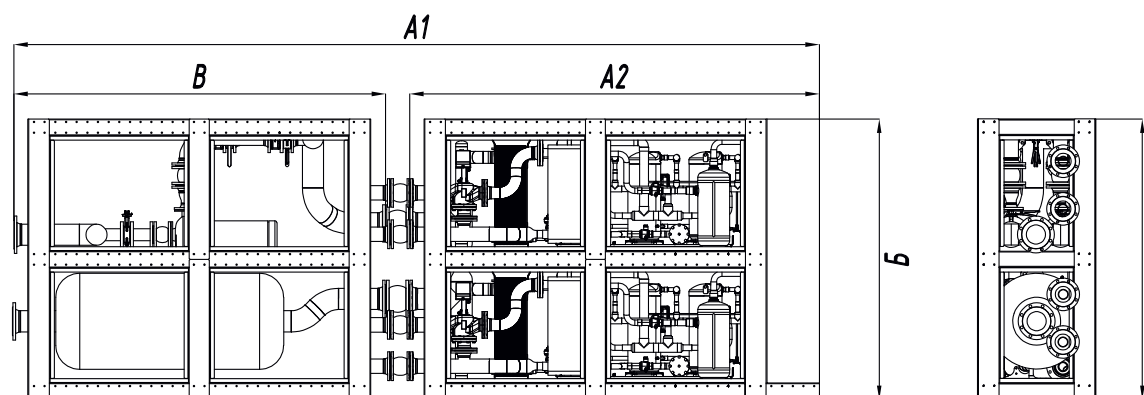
Габаритные размеры двухконтурных чиллеров (с гидромодулем) LM COOL SPP.
